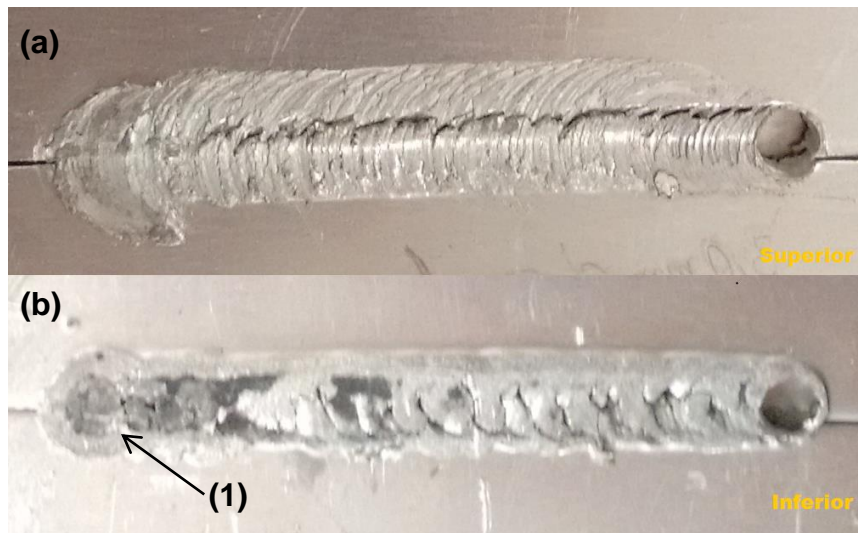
Ensaio de solda com rotação de 1200 RPM e avanço de 45 mm/min. Vistas (a) superior e (b) inferior da solda.
